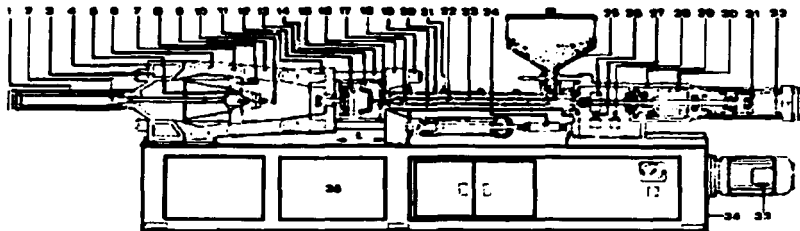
Sección longitudinal de una máquina de moldeo por inyección por husillo reciprocante del tipo doble rodilera. Nótese el molde y el husillo (22) en posición al final de la inyección. 1. Cilindro hidráulico del molde 2. Pistón que actúa el cierre del molde 3. Tuerca de la cabeza de moldes 4. Cabeza de moldes 5. Cabeza de cruz 6. Biela corta 7. Perno 8. Leva de empuje 9. Biela larga 10. Botador de expulsión de la pieza 11. platina móvil 12. Medio molde móvil 13. Medio molde fijo 14. Columna 15. Boquilla libre 16. Platina fija 17. Válvula anti-retorno 18. Tuerca de la platina fija 19. Cilindro para accionar el movimiento del grupo de inyección 20. Resistencia de calentamiento del cilindro de plastificación 21. Termopar 22. Husillo de plastificación 23. Cilindro de plastificación 24. Tuerca para la regulación de la posición de la boquilla 25. Tolva 26. Acoplamiento (husillo-eje-motor) 27. Interruptor de límite para accionar la segunda presión de inyección 28. Interruptor de límite para actuar el término de plastificación 29. Cabeza de inyección 30. Motor hidráulico para actuar la rotación del husillo 31. Pistón de inyección 32. Cilindro de inyección 33. Motobomba del sistema hidráulico 34. Bancada (base) 35. Abertura para recolectar las piezas moldeadas.
